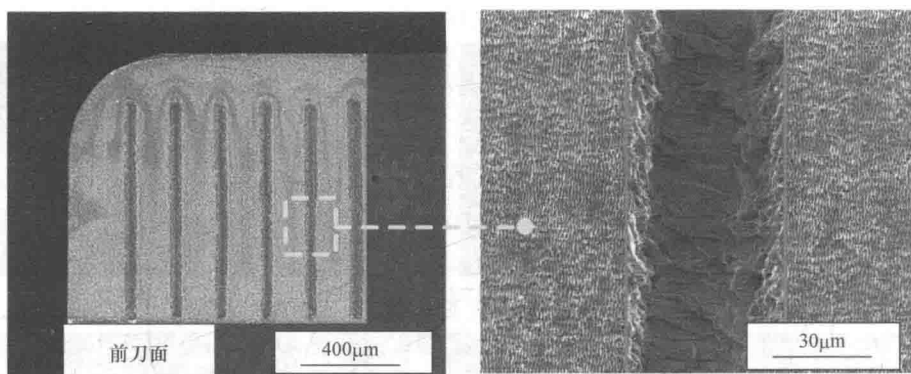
硬质合金刀具表面激光加工的微纳复合织构形貌
